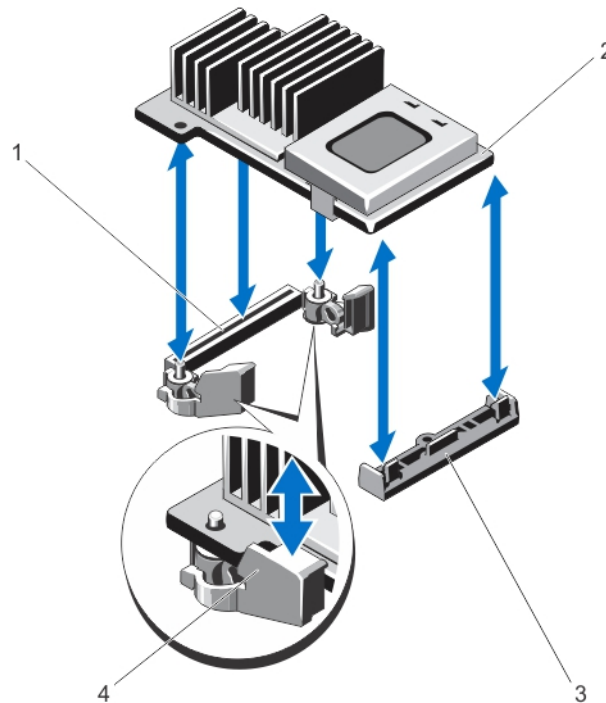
Retrait de la carte contrôleur de stockage intégrée
